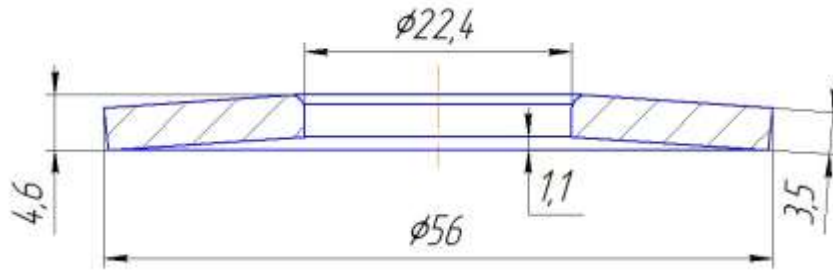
Пружина предохранителя по усилию прессы КД2124
